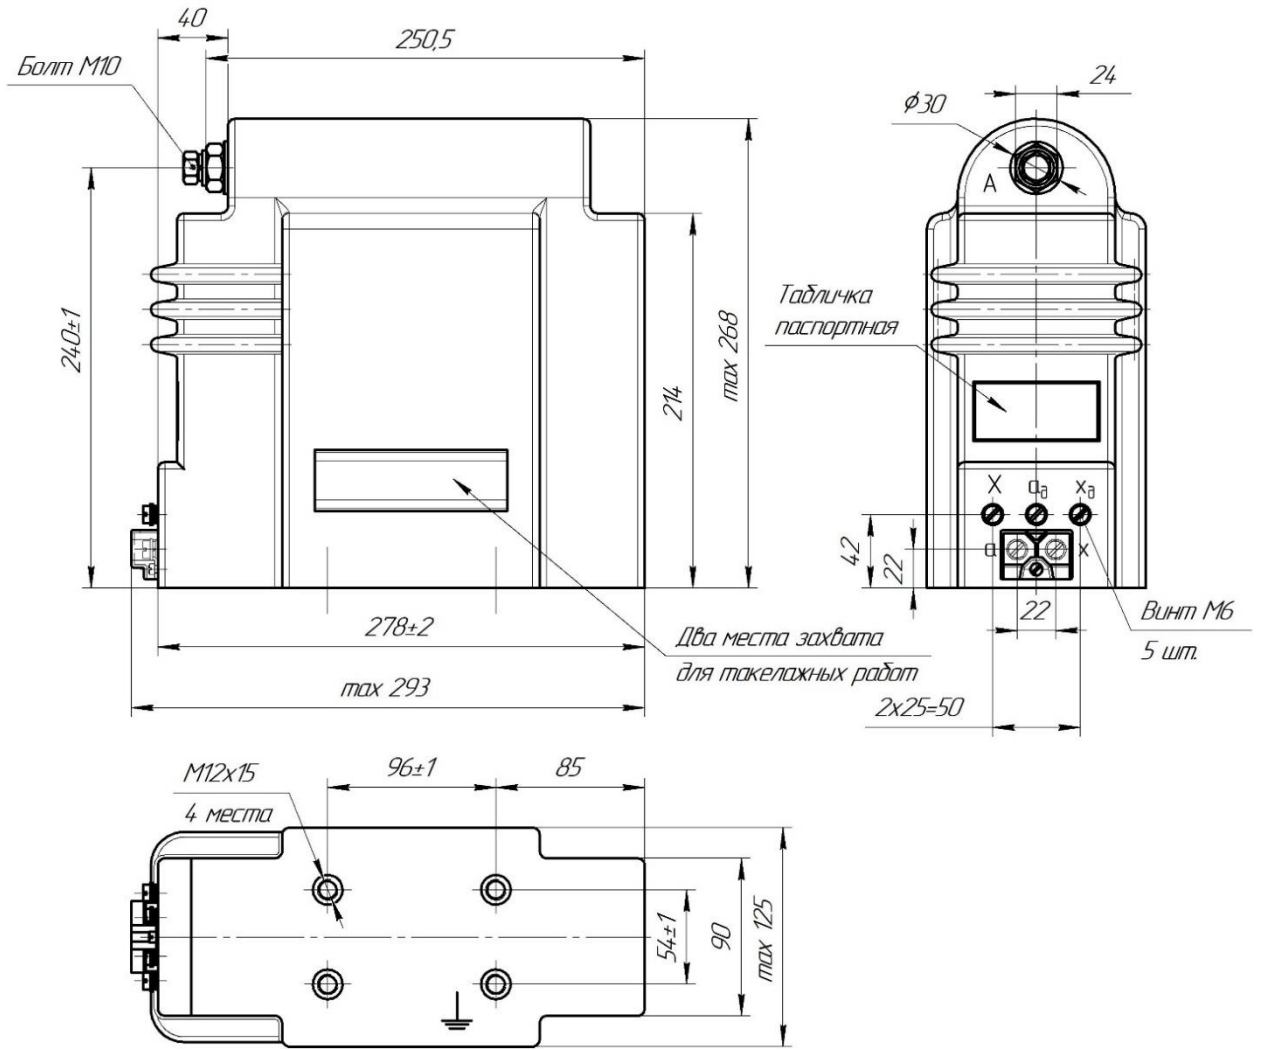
Габаритные, установочные и присоединительные размеры трансформаторов напряжения ЗНОЛ-СЭЦ-6-21 и ЗНОЛ-СЭЦ-10-21
